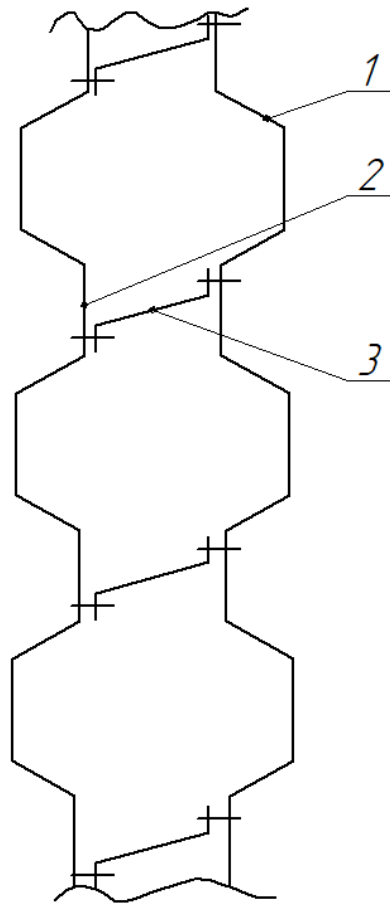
Багатошарова обшивка несучого кузова
